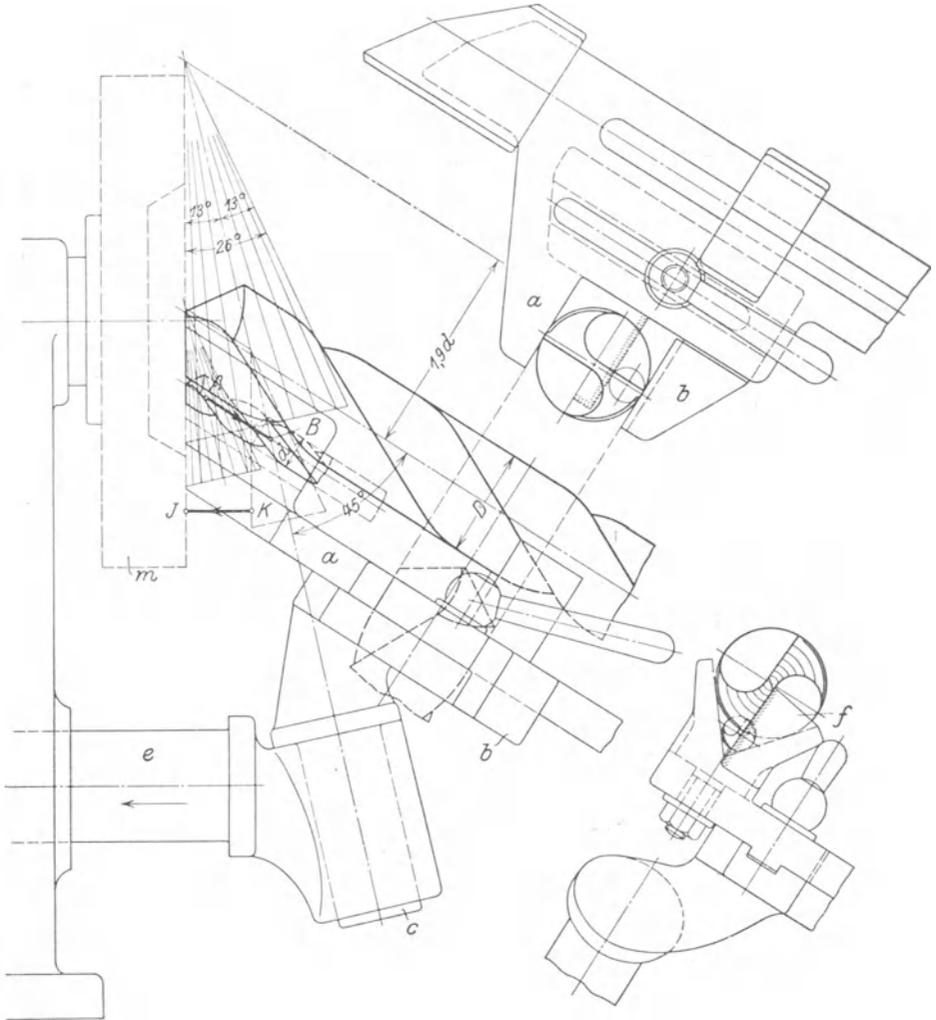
Bewegung des Bohrers bei der Washburne-Maschine.
